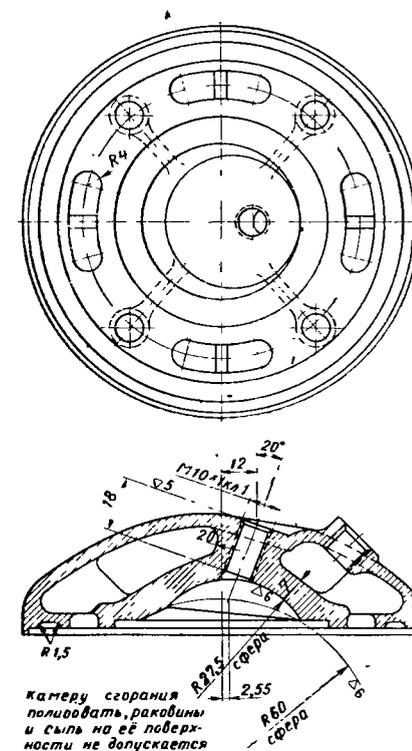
Головка цилиндра двухтактного гоночного двигателя С2—125.
